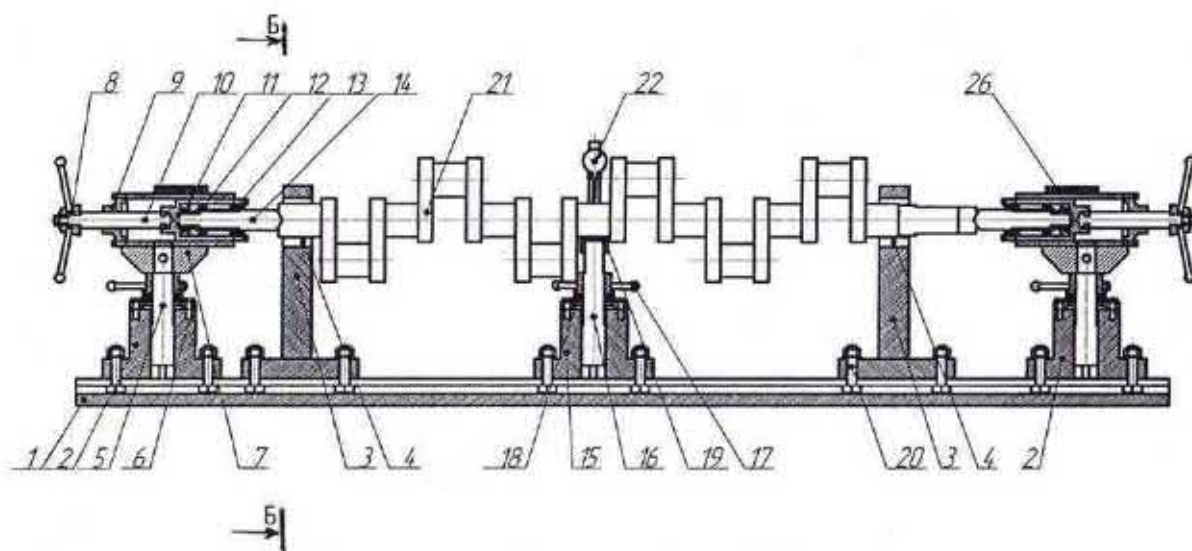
Новое устройство для проверки биения коленвала по центрам и выпрямления на гидравлическом прессе
